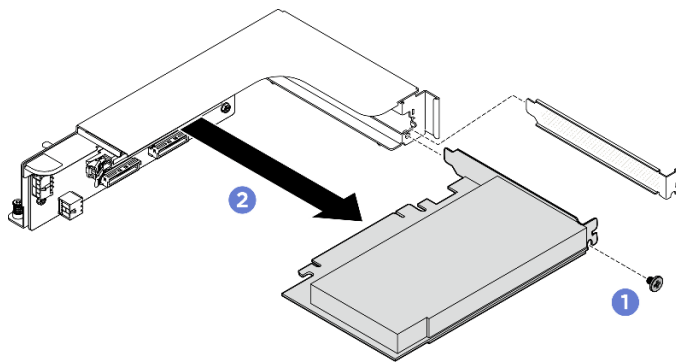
Entfernen des hinteren PCIe-Adapters
